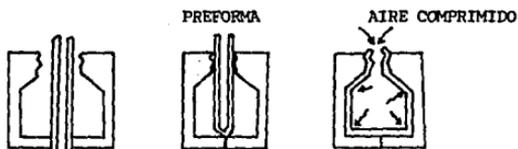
MOLDEADO POR SOPLADO (II).
